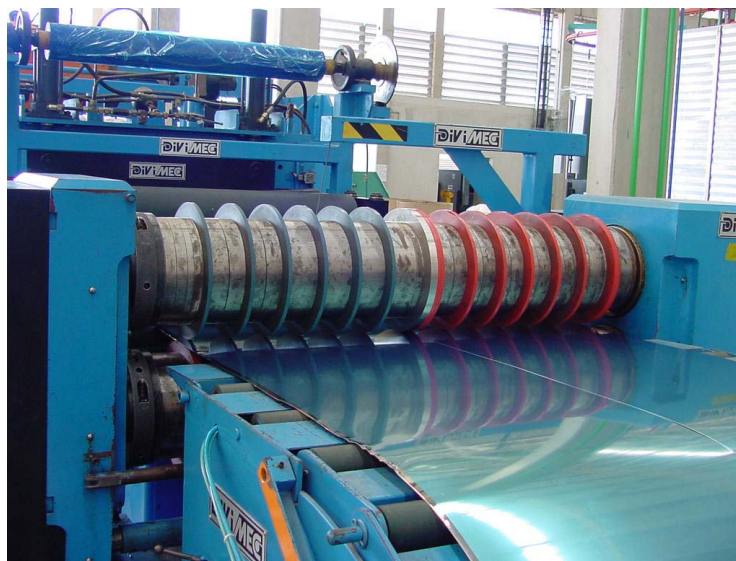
Máquina Slitter realizando corte de bobinas com largura L.
